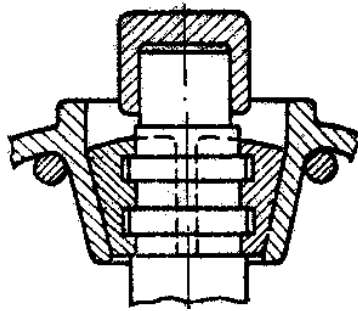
Встановлення твердосплавного ковпачка на стрижень клапана
